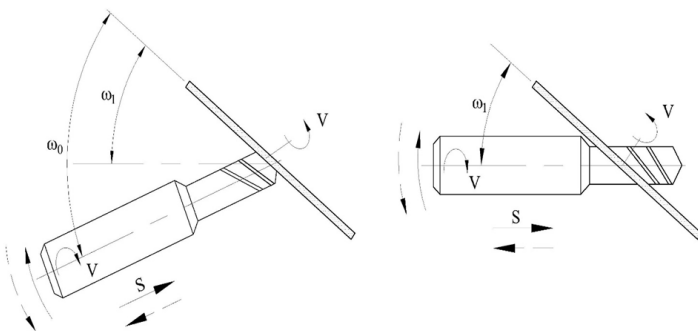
Схема изменения ориентации осей заготовки сверла и шлифовального круга методом поворота оси шпинделя заготовки.
